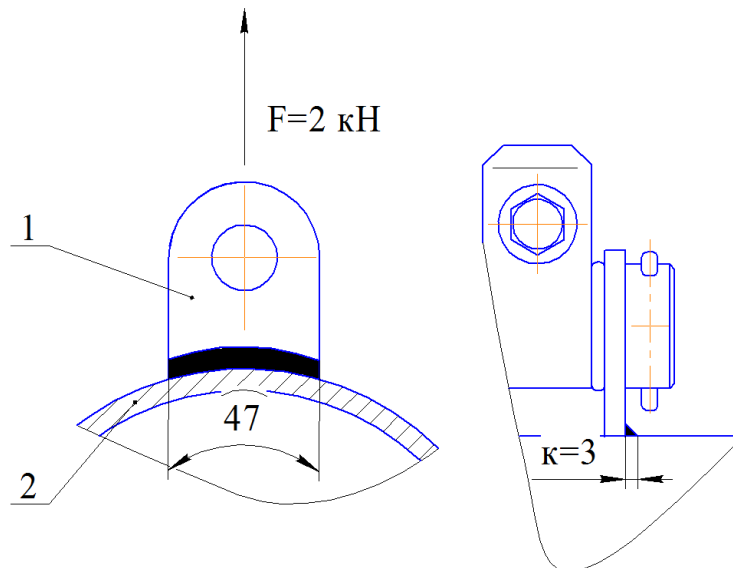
Схема зварного з'єднання : 1 – вухо; 2 – труба.
